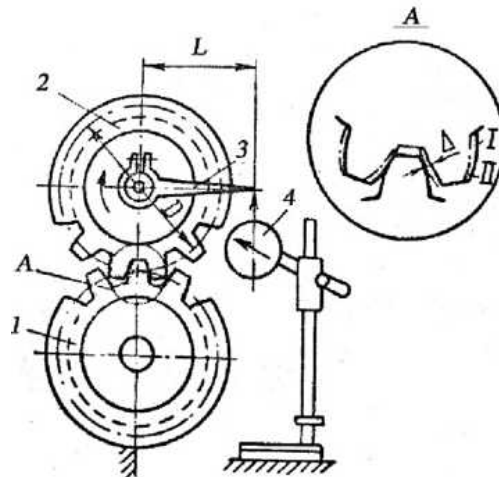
Контроль бокового зазору в зачепленні циліндричних зубчастих коліс: 1– нижня шестерня; 2 – зубчасте колесо; 3 – хомут; 4 – індикатор; I-II – положення зубчастого колеса.
